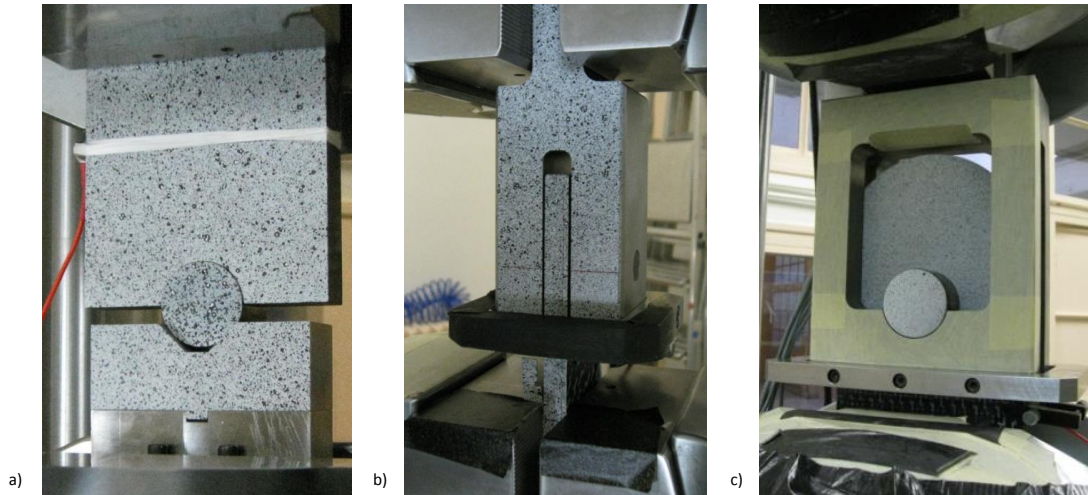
Dispositifs expérimentaux pour l'étude de la défaillance de chapes et assemblages composites de forte épaisseur. a) Essai de compression sur demi-trou. b) Essai en double recouvrement. c) Essai en double recouvrement avec flasques ajourés.
